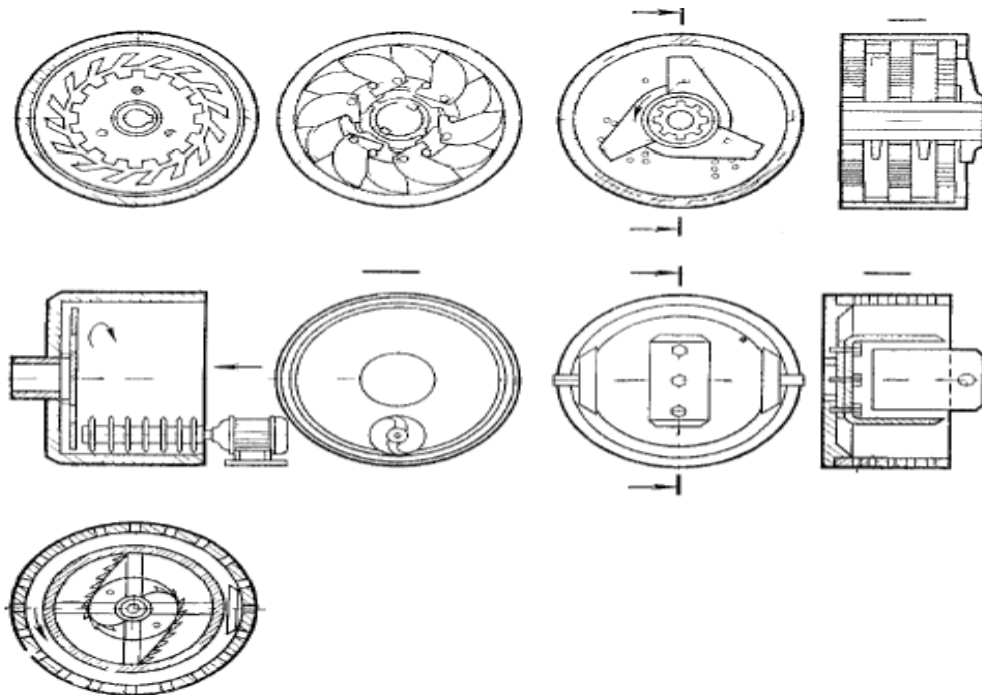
Схема пристроїв подрібнення: а - роторний тип; б, в – тип із багатьох ножів; г – багато дисків; д - барабанний; е - комбінований
